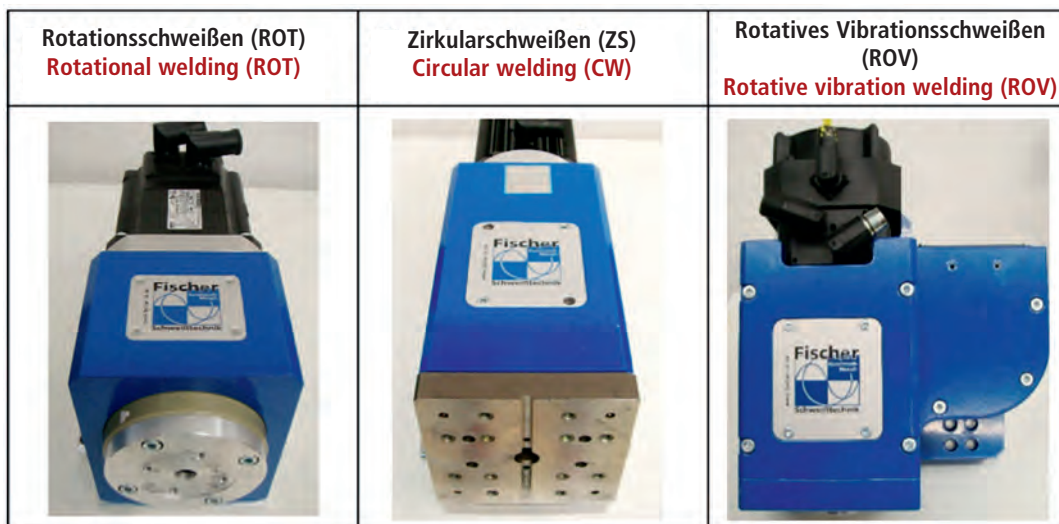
Fotos der drei verwendeten Fügemodule, von links nach rechts; Rotationsschweißen, Zirkularschweißen, ROV-Schweißen
